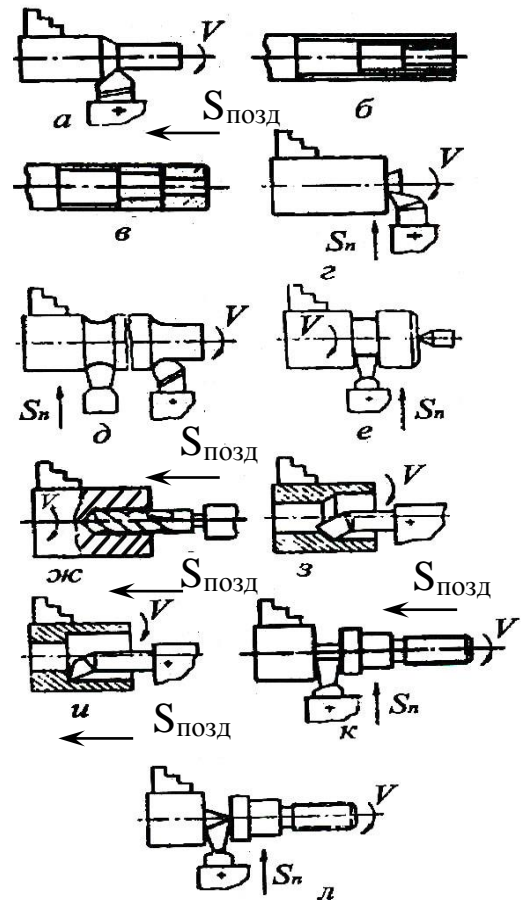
Схеми обробки заготовок на токарно-гвинторізних верстатах
